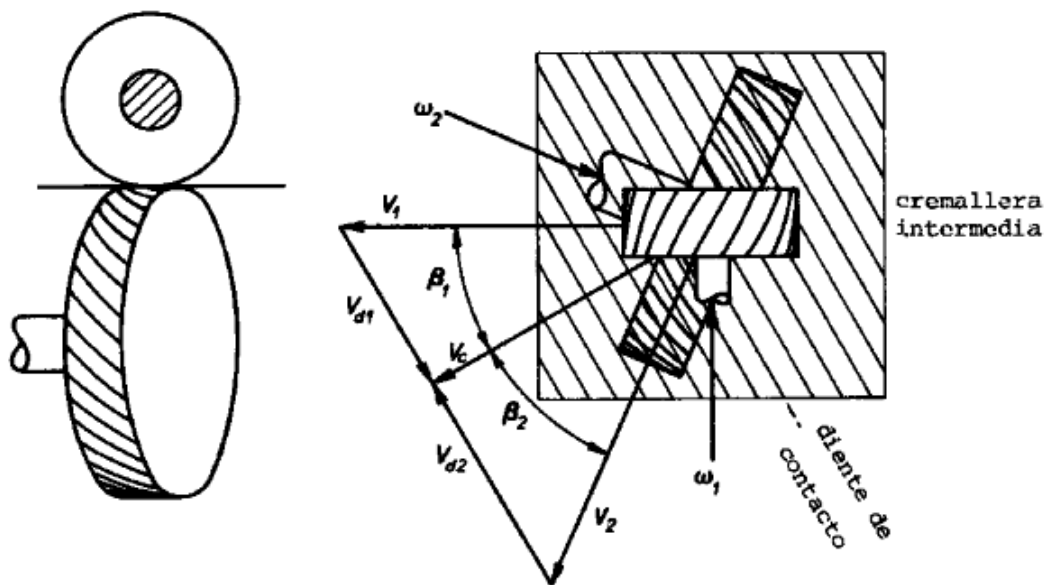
Engranaje helicoidal entre ejes que se cruzan
